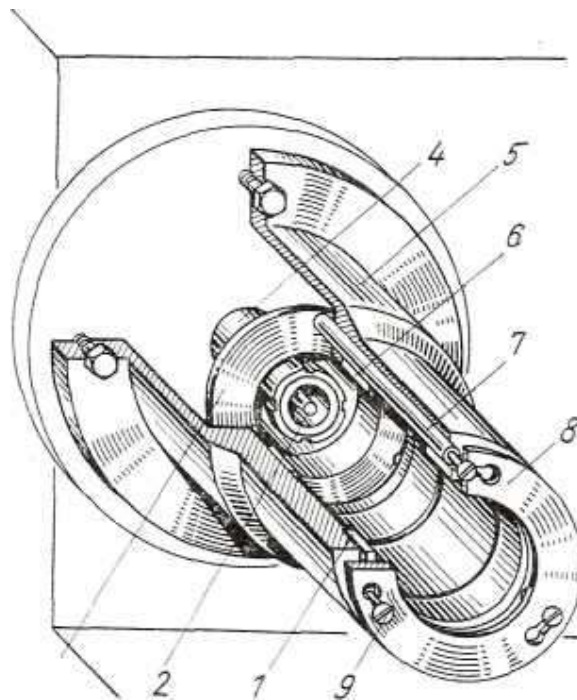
Пристрій для установки гільзи при шліфуванні робочої поверхні [4]:
